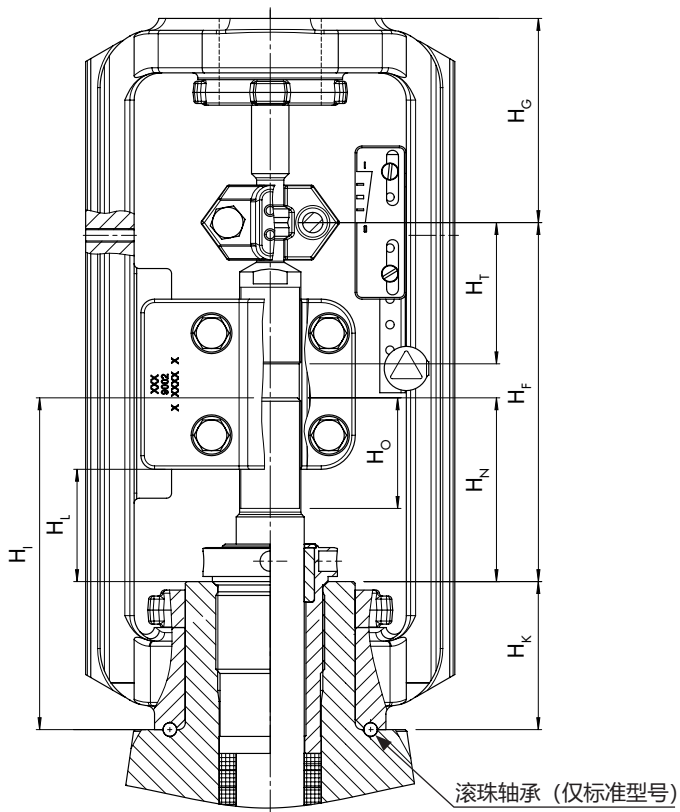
3271 型和 3277 型气动执行机构尺寸图, 含安装尺寸
